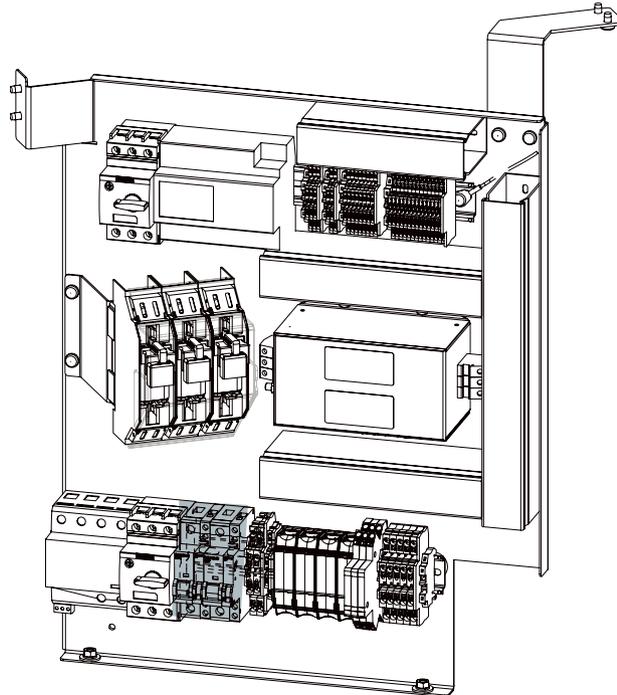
Anschlüsse für die Hilfsstromversorgung
